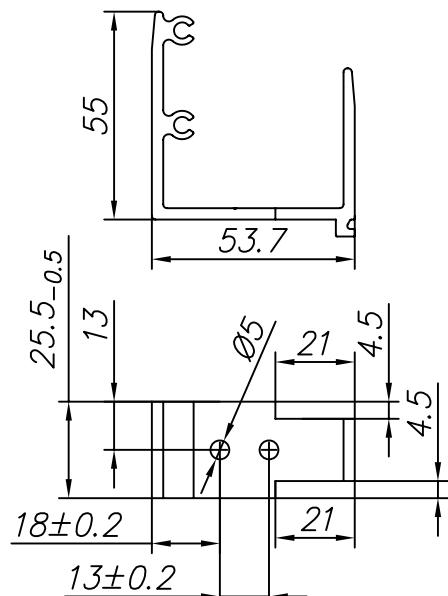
Изготовление соединителя FLGU.400.0913
